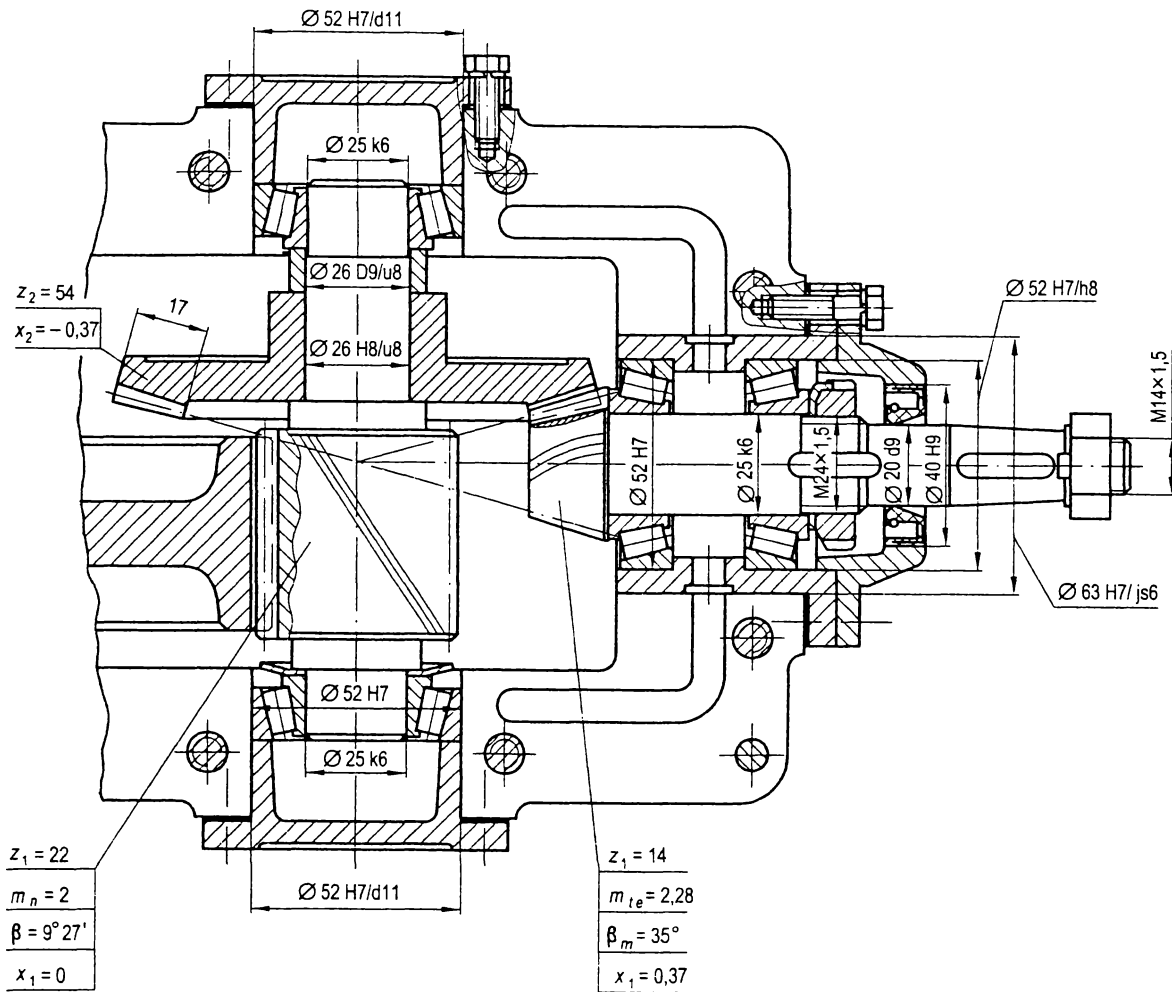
Пример конструкции вала-шестерни конической передачи коническо-цилиндрического зубчатого редуктора [1]
